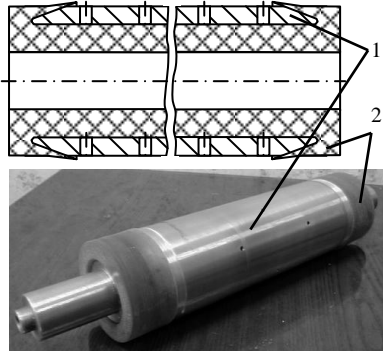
Схема конструкції та загальний вигляд армованого еластичного вкладиша: 1 – вставка армуюча; 2 – вкладиш еластичний
